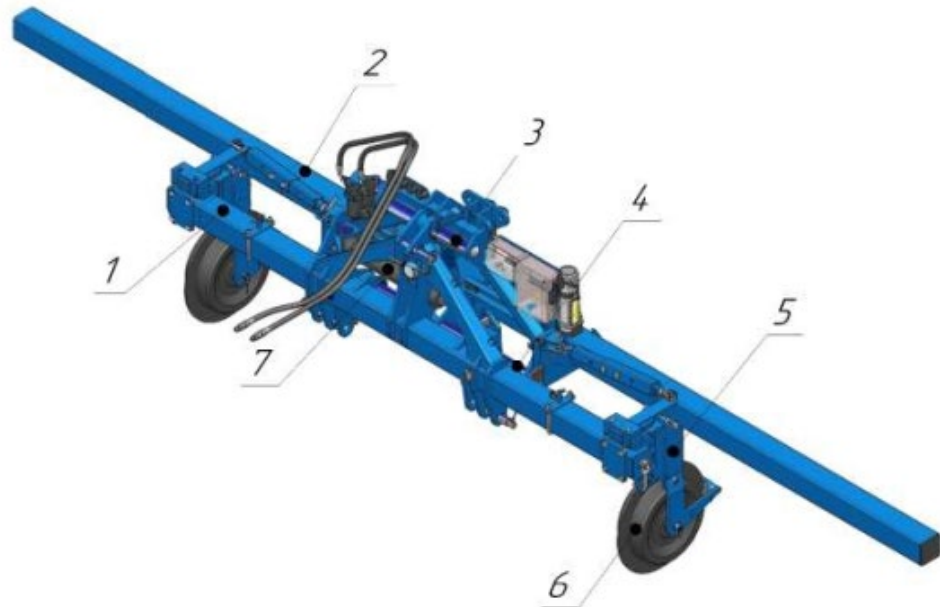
Плаваючий навісний пристрій фірми Carre:
